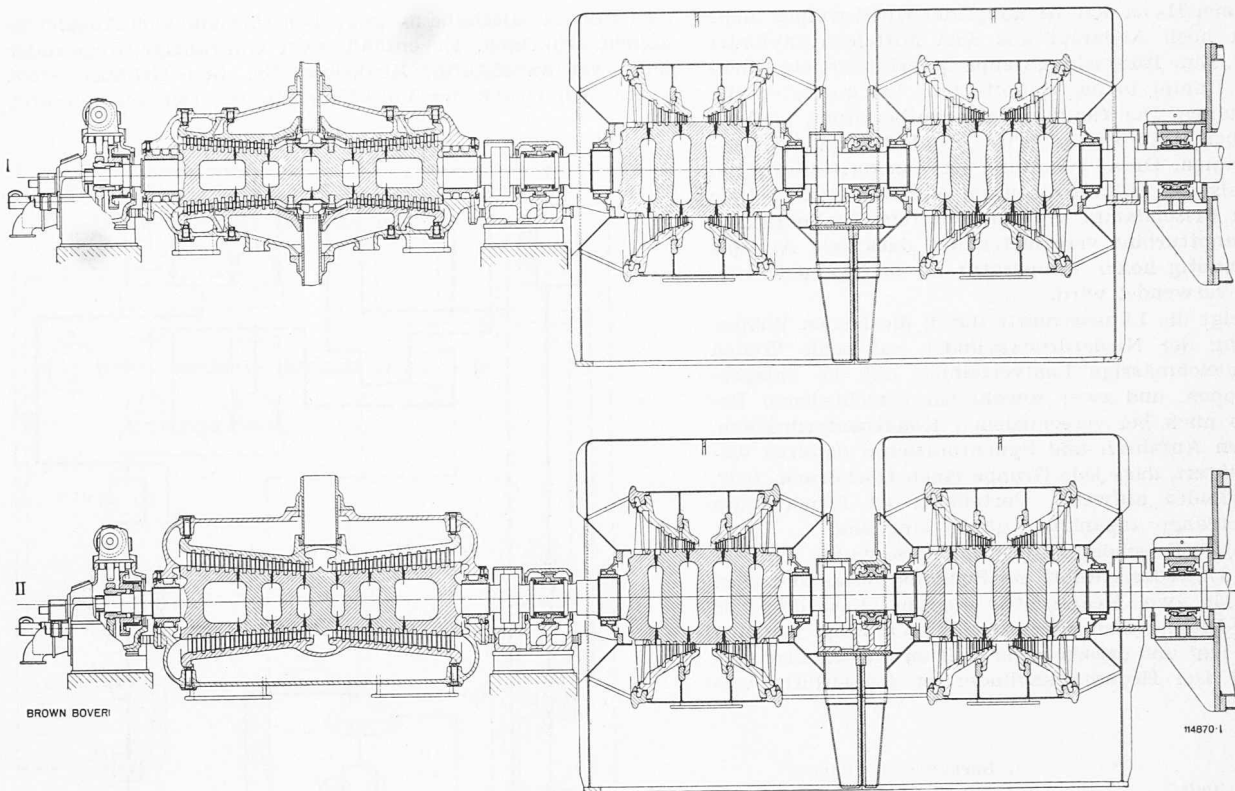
Längsschnitt durch die 500-MW-Dampfturbine für die TVA
